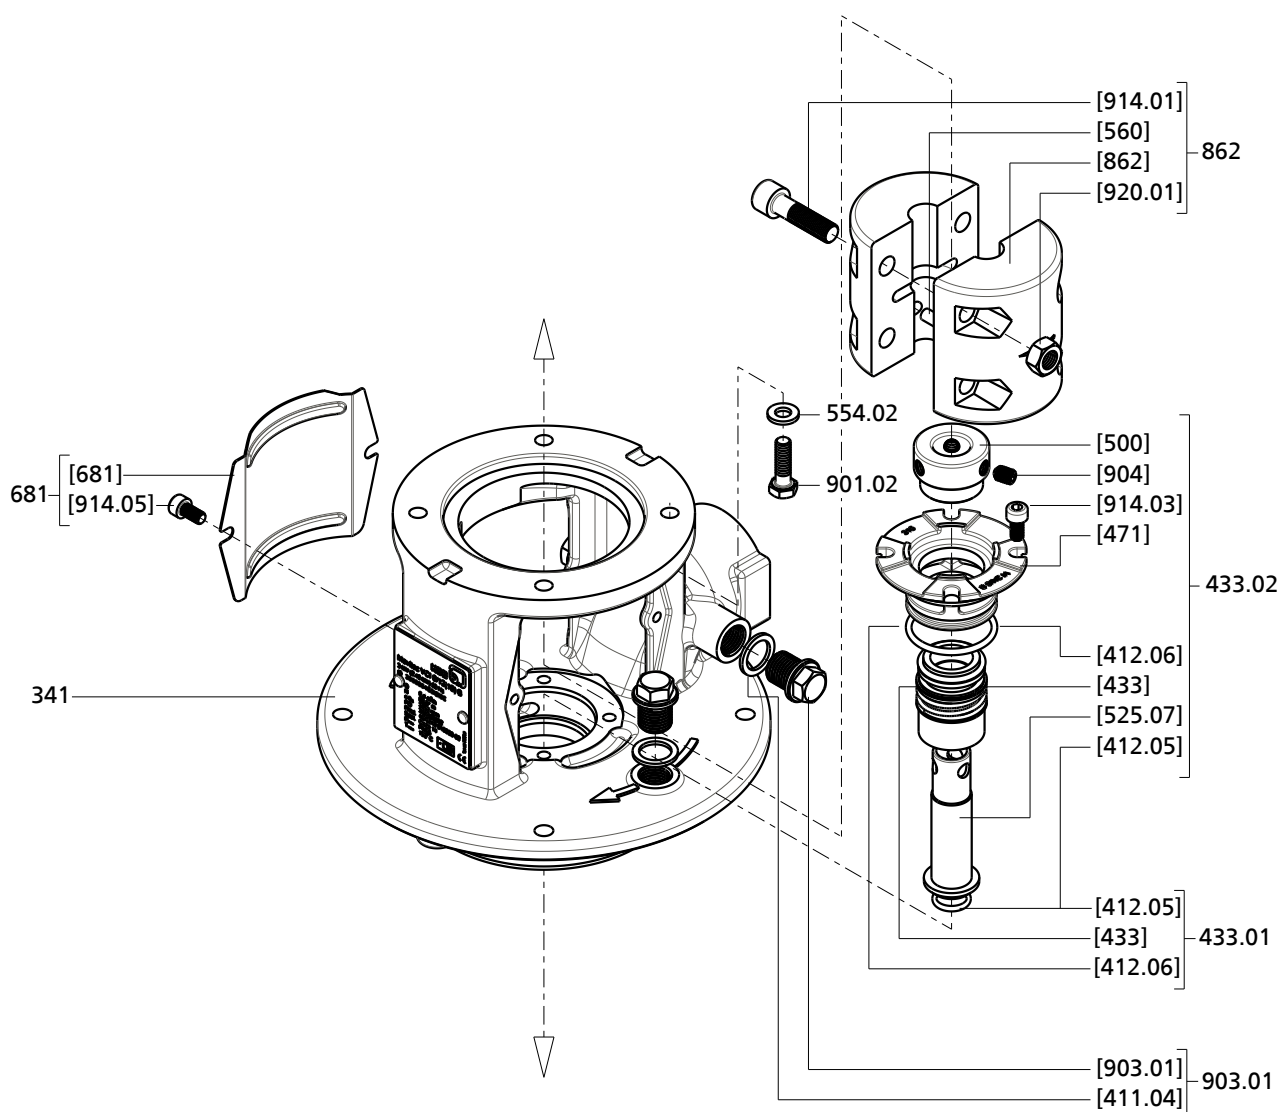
Покомпонентный сборочный чертеж фонаря привода с торцовым уплотнением [детали в квадратных скобках поставляются только в упакованных комплектах]
